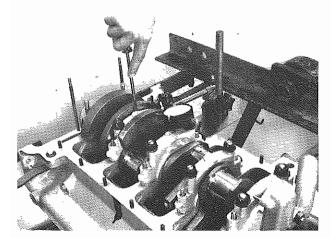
Verificare il gioco assiale Checking axial clearance
